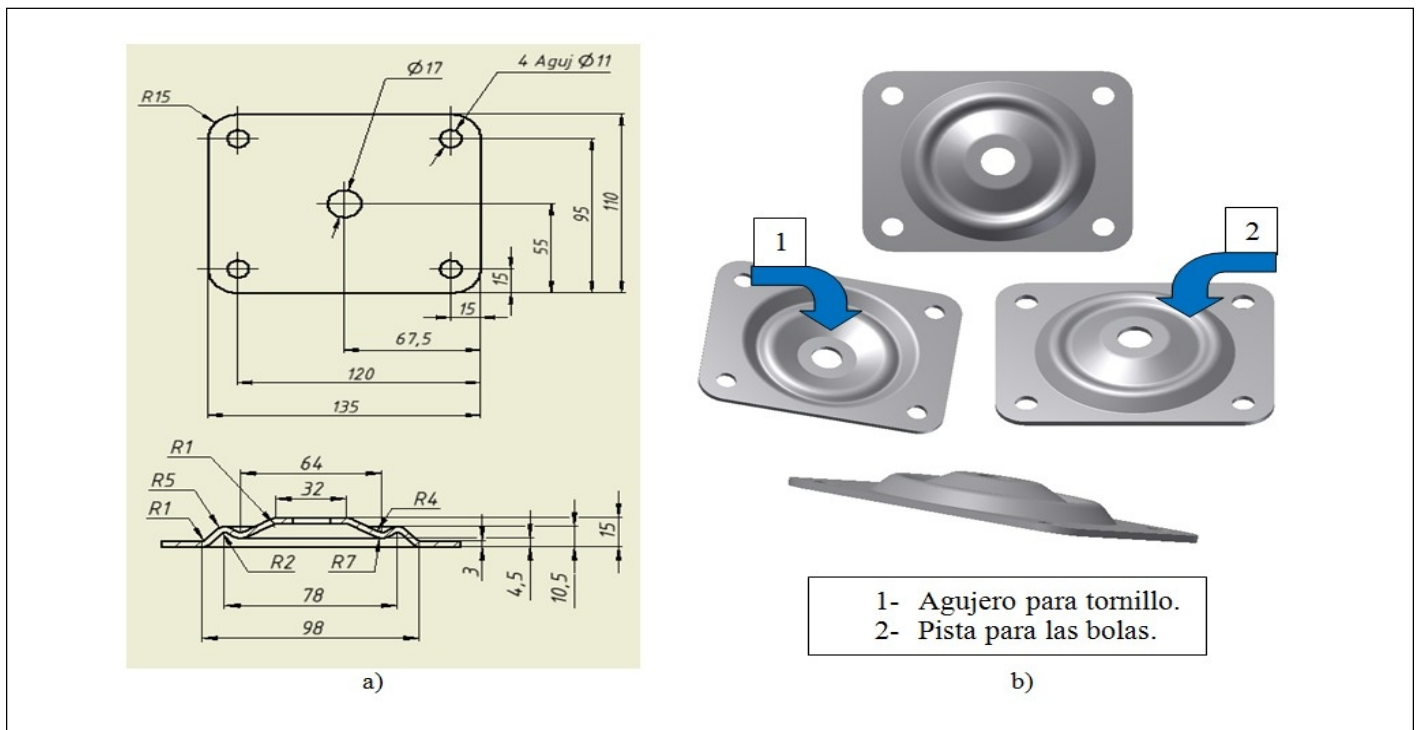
Geometría del platillo: a) Dimensiones; b) Vistas en 3D
